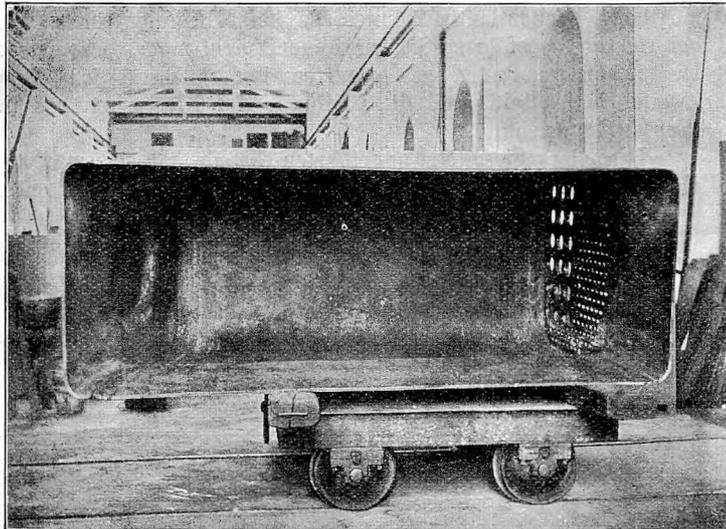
Fertig geschweißte Feuerbüchse. Innenansicht.
